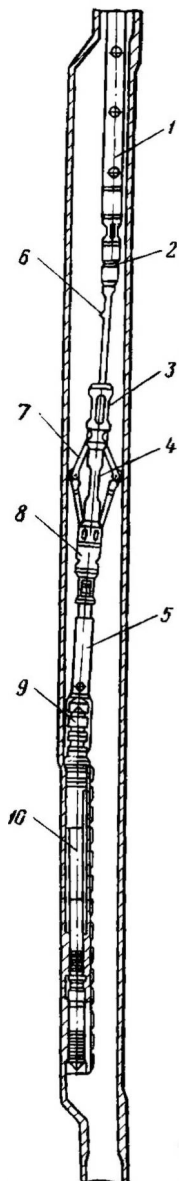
Подземное оборудование при замене газлифтного клапана в вертикальной скважине: 1 — механический ясс; 2 — шарнирное соединение; 3 — верхняя подвижная гильза; 4 — отклонитель рычажного типа; 5 — короткая штанга; 6 — упор на отклонителе; 7 — рычаги; 8 — нижняя подвижная гильза; 9 — ловильная головка фиксатора газлифтного клапана; 10 — газлифтный клапан
